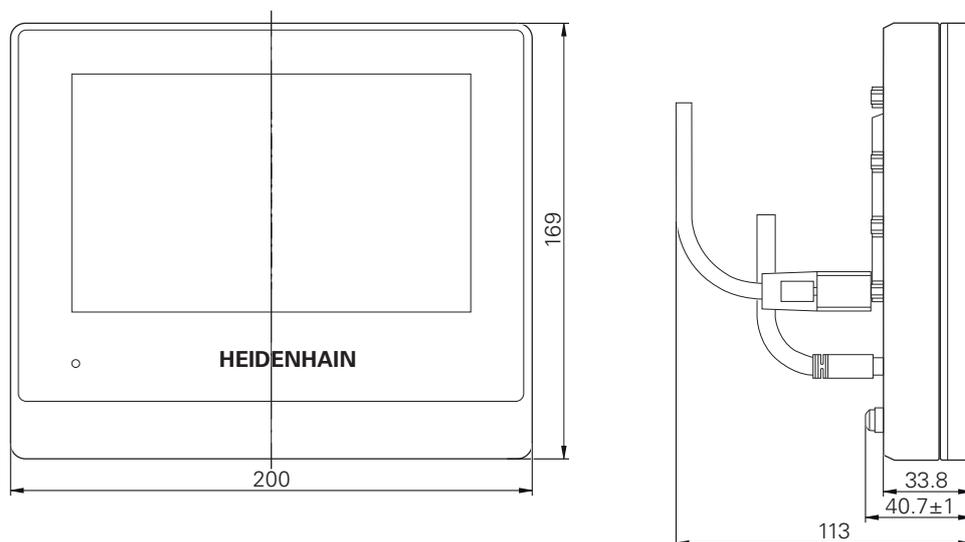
Размеры корпуса устройств с ID 1089178-xx
